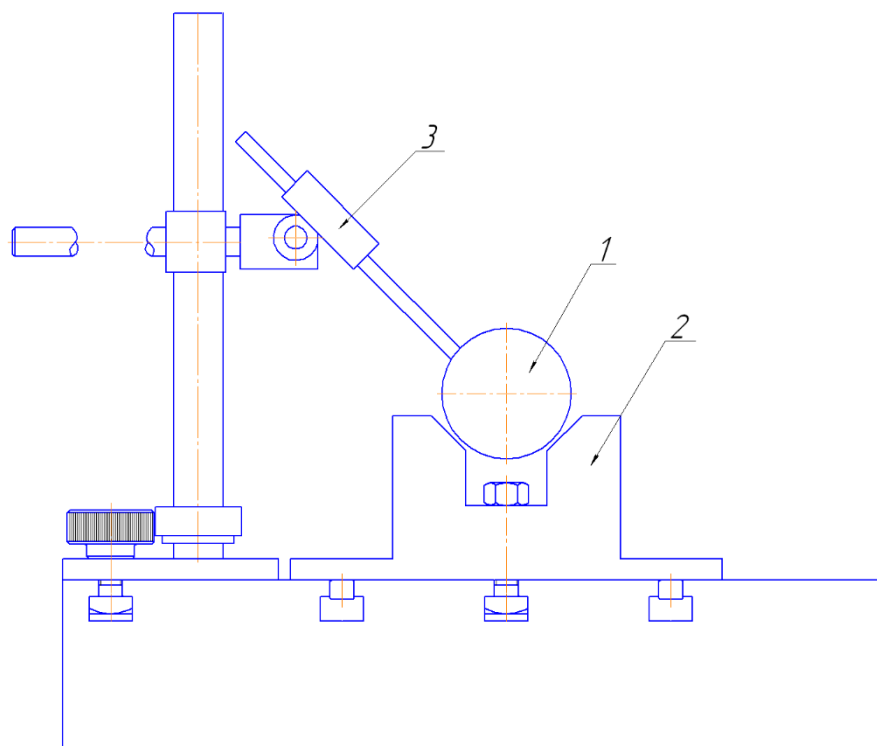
Контрольно-измерительный прибор (вид сбоку):
